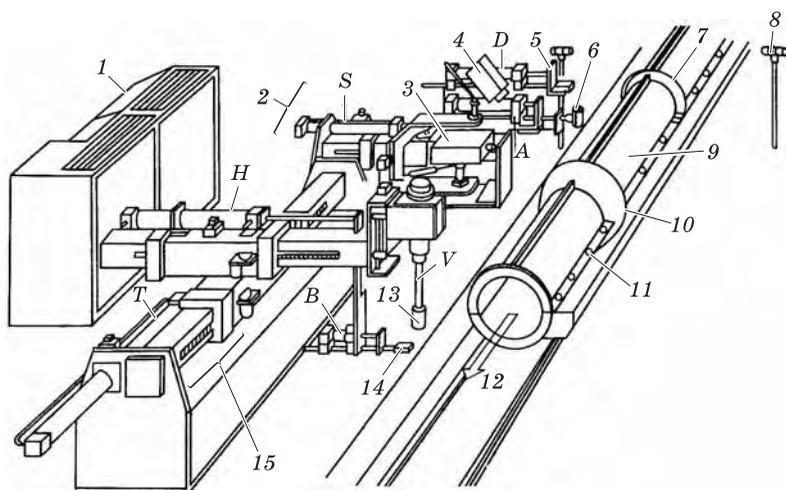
Компоновка роботизированного сборочного комплекса для винтового соединения полуформ:
